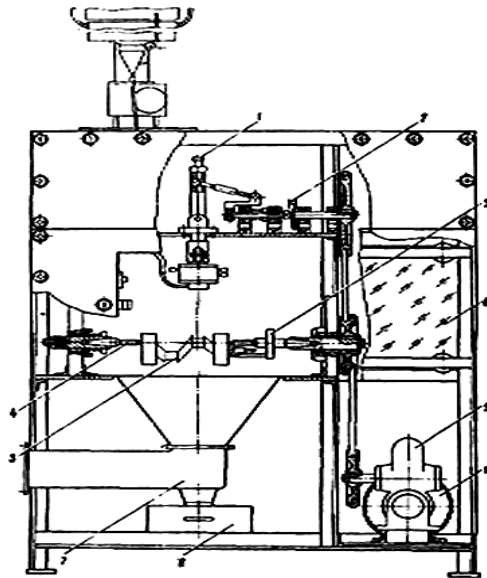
Верстат для плазмової металізації зовнішніх циліндричних поверхонь деталей
